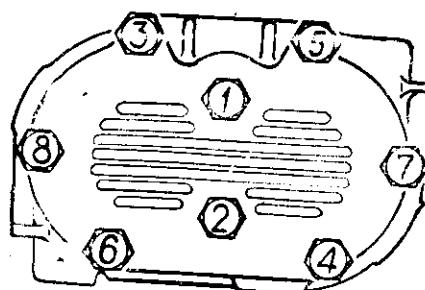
Порядок затяжки гаек крепления головки блока компрессора
